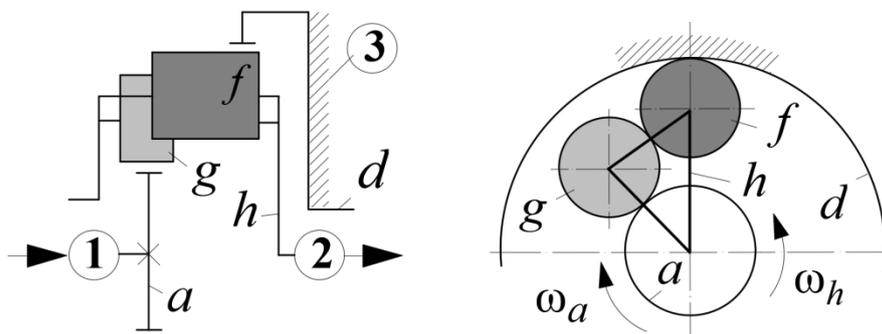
Схема трехзвенного планетарного механизма с реверсным сателлитом
